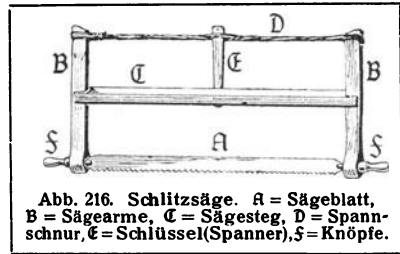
Schlitzsäge. A = Sägeblatt, B = Sägearme, C = Sägesteg, D = Spannschnur, E = Schlüssel (Spanner), S = Knöpfe.
